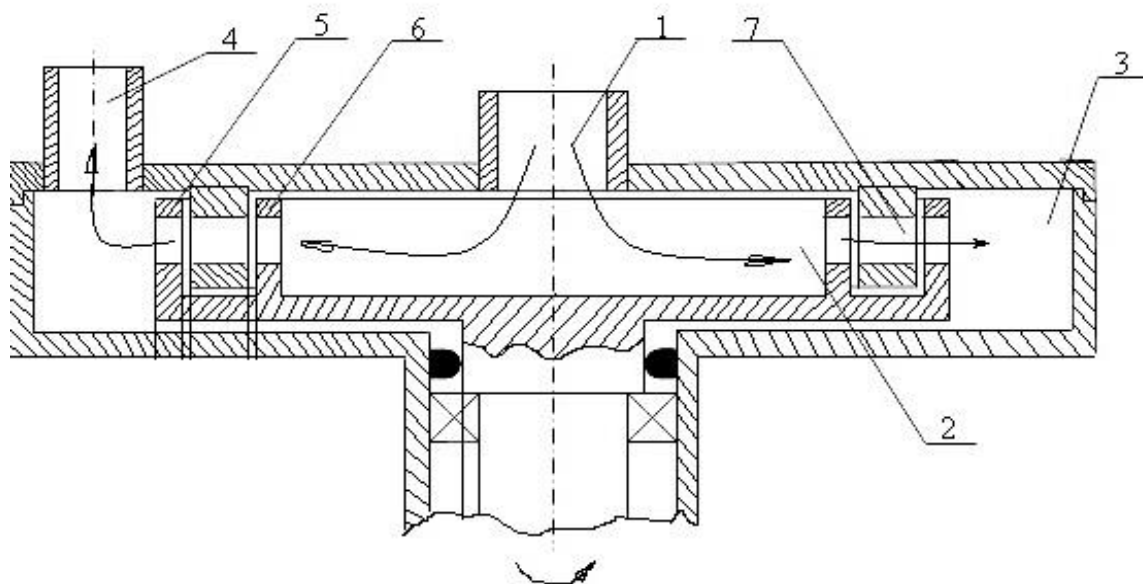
Схема модифікованого роторного апарату: 1 – вхідний патрубков; 2 – порожнина ротора; 3 – робоча камера; 4 – вихідний патрубков; 5 – канал зовнішнього ротора; 6 – канал внутрішнього ротора; 7 – канал статора
